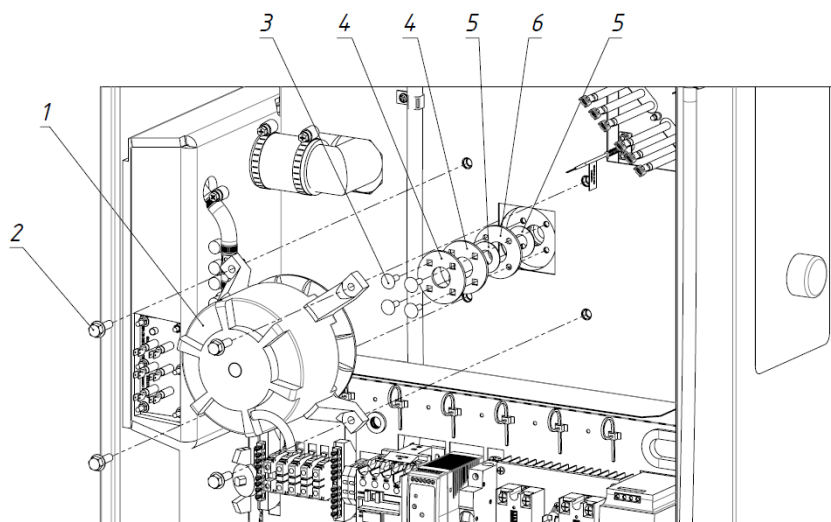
Конструктивные размеры соединения крыльчатки вентилятора с осью электродвигателя
